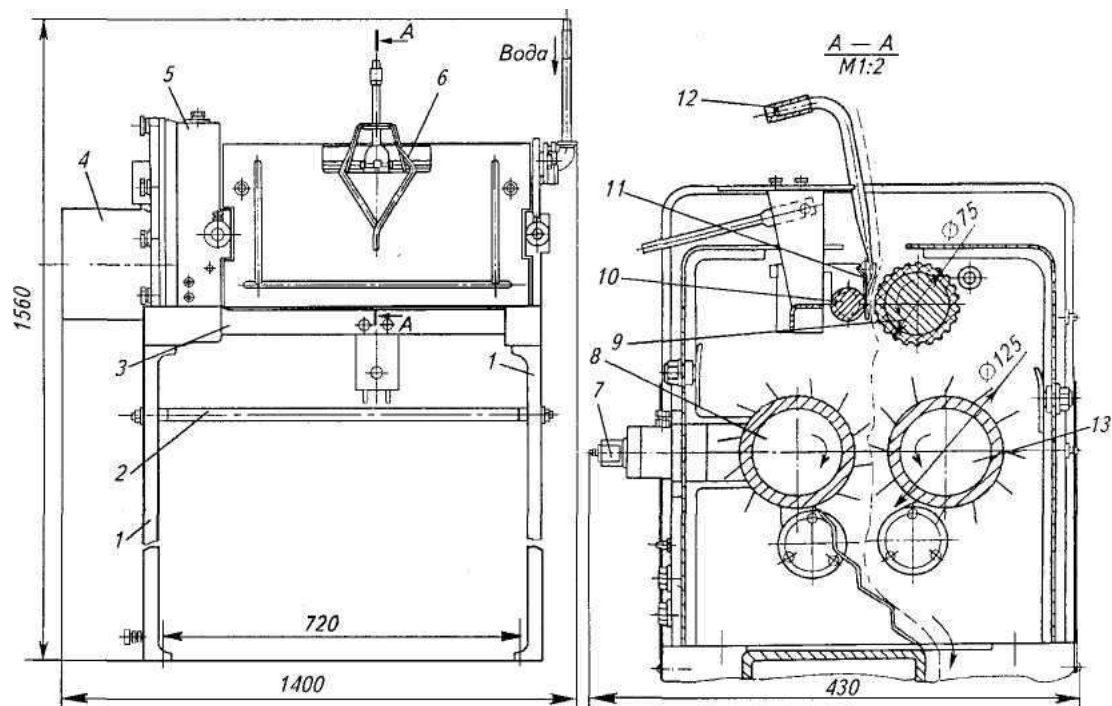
Шлямодробильна машина К6-ФОК-2-К-02: 1 – стійки; 2 – стяжка; 3 – плита; 4 – електродвигун; 5 – редуктор; 6 – напрямна; 7 – гвинтовий механізм регулювання зазору; 8, 13 – пластинчасті вальці; 9 – подавальний рифлений валик; 10 – ексцентриковий вал; 11 – пластина; 12 – опора шнекового транспортера
